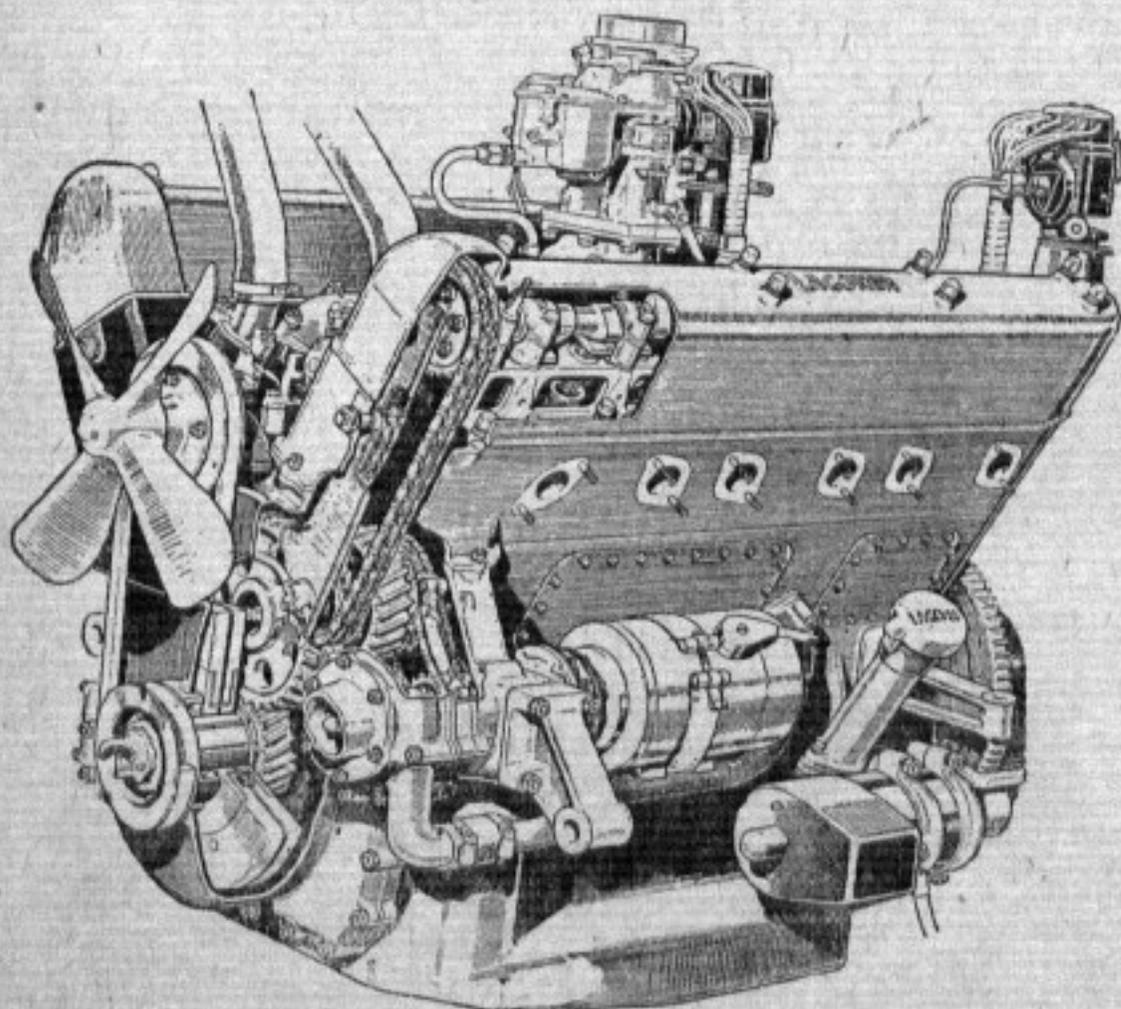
Двенадцатицилиндровый V-образный двигатель Лагонда
